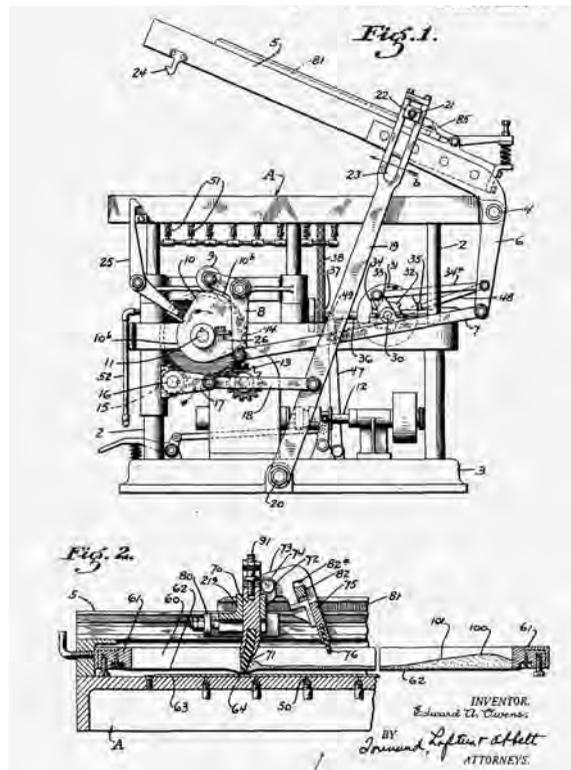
E. A. Owens. *Stencil Printing Machine*. (1933). Máquina con base aspirante y mecanismo de raqueta y contrarraqueta. Anexo 1. Pat. 1.922.710
